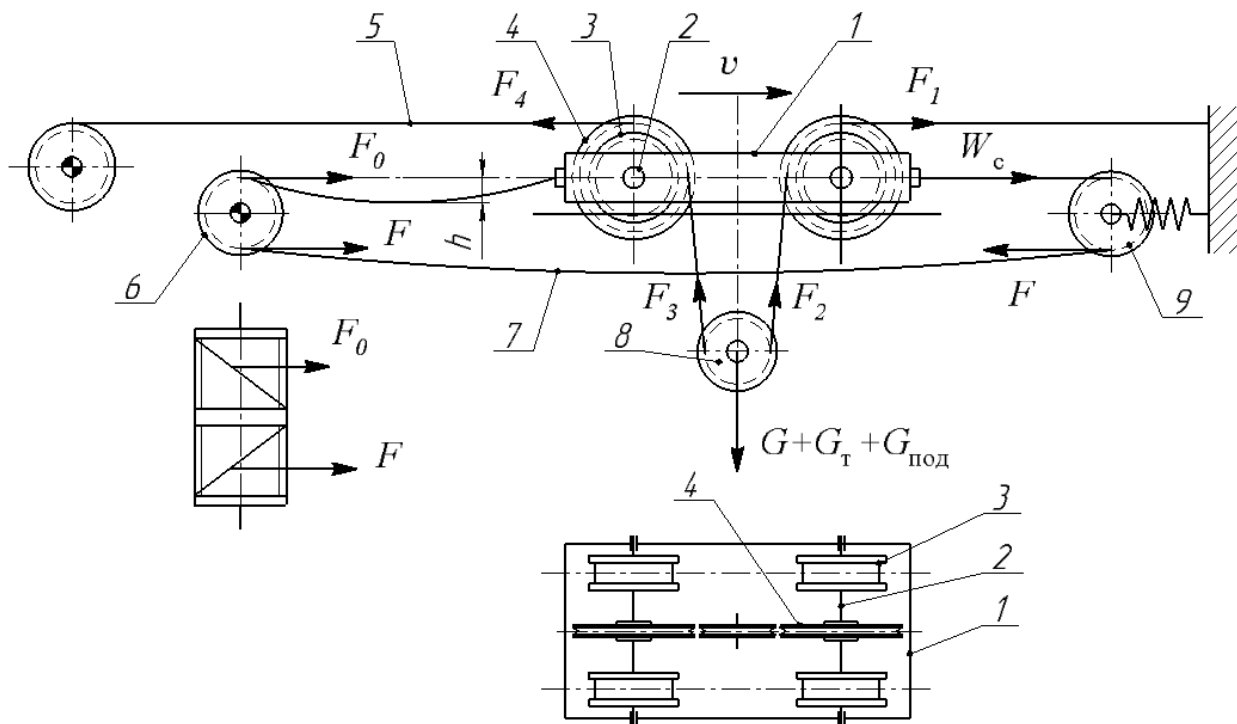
Схема механизма передвижения тележки с канатной тягой: 1 — рама тележки; 2 — ось блоков и ходовых колес; 3 — ходовое колесо; 4 — блок механизма подъема; 5 — подъемный канат; 6 — барабан механизма передвижения; 7 — тяговый канат; 8 — блок подвески; 9 — обводной блок
